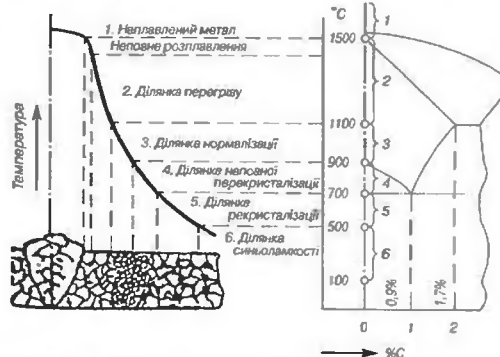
Будова зони термічного впливу зварного з'єднання
